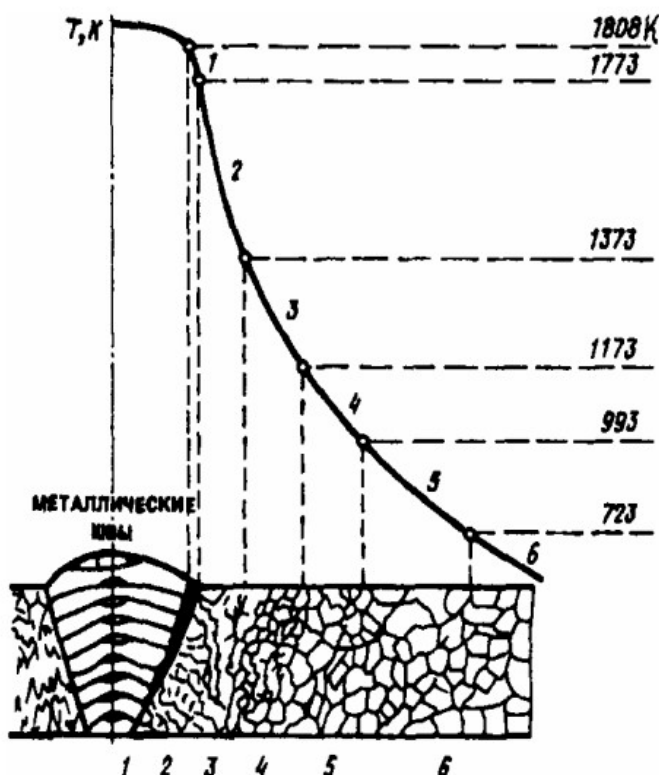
Зоны термического влияния сварного шва малоуглеродистой стали
